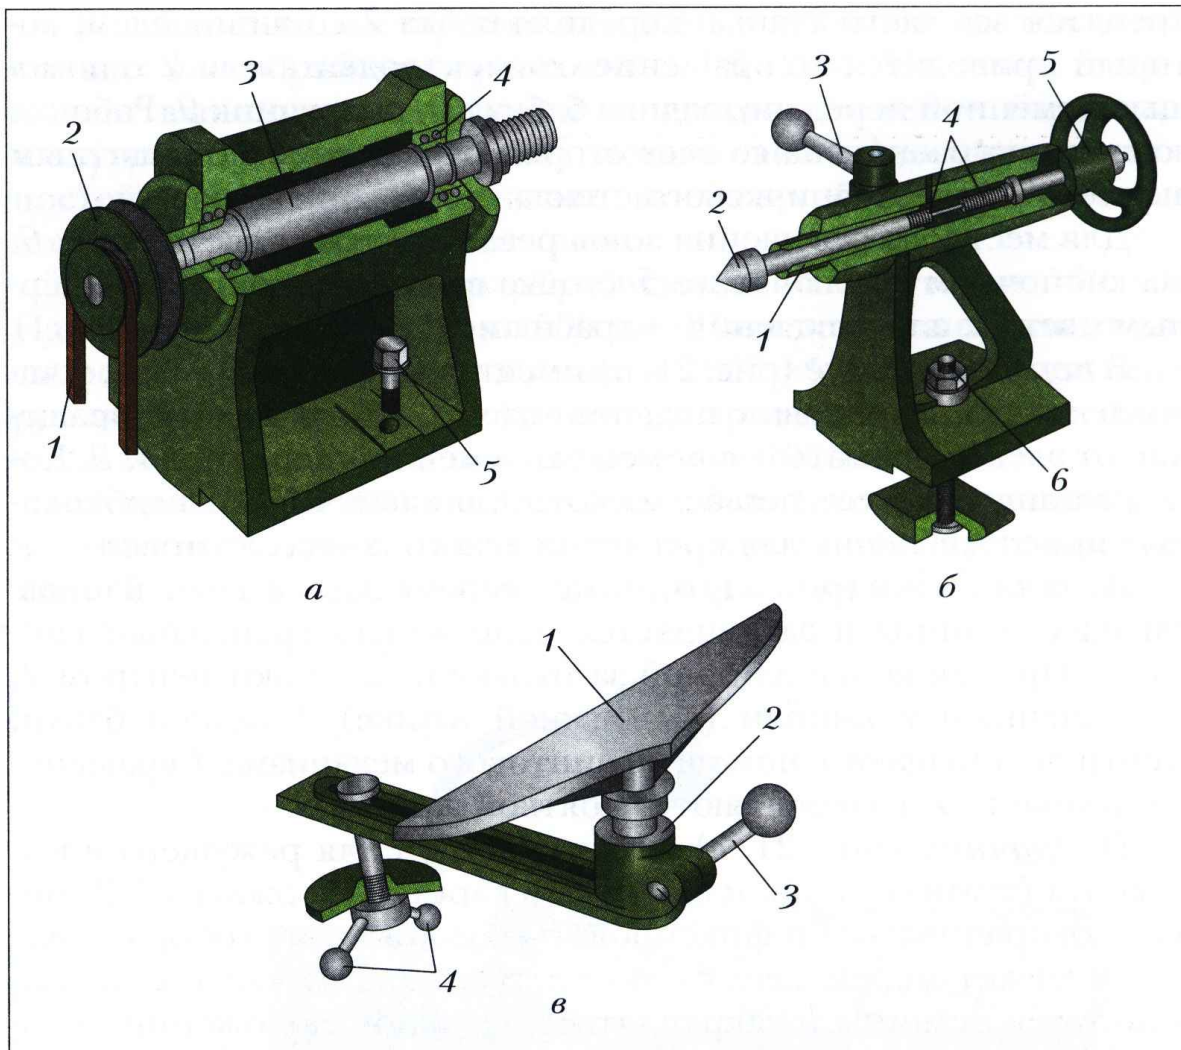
Основные части станка СТД-120М: *a* – передняя бабка: 1 – клиновой ремень ремённой передачи; 2 – двухступенчатый шкив; 3 – шпиндель; 4 – подшипник шариковый; 5 – крепёжный винт; *б* – задняя бабка: 1 – пиноль; 2 – центр; 3 – рукоятка зажима; 4 – винтовой механизм; 5 – маховик; 6 – крепёжный винт; *в* – подручник в сборе: 1 – подручник; 2 – каретка (держатель); 3 – рукоятка стопора; 4 – рукоятки крепления каретки
